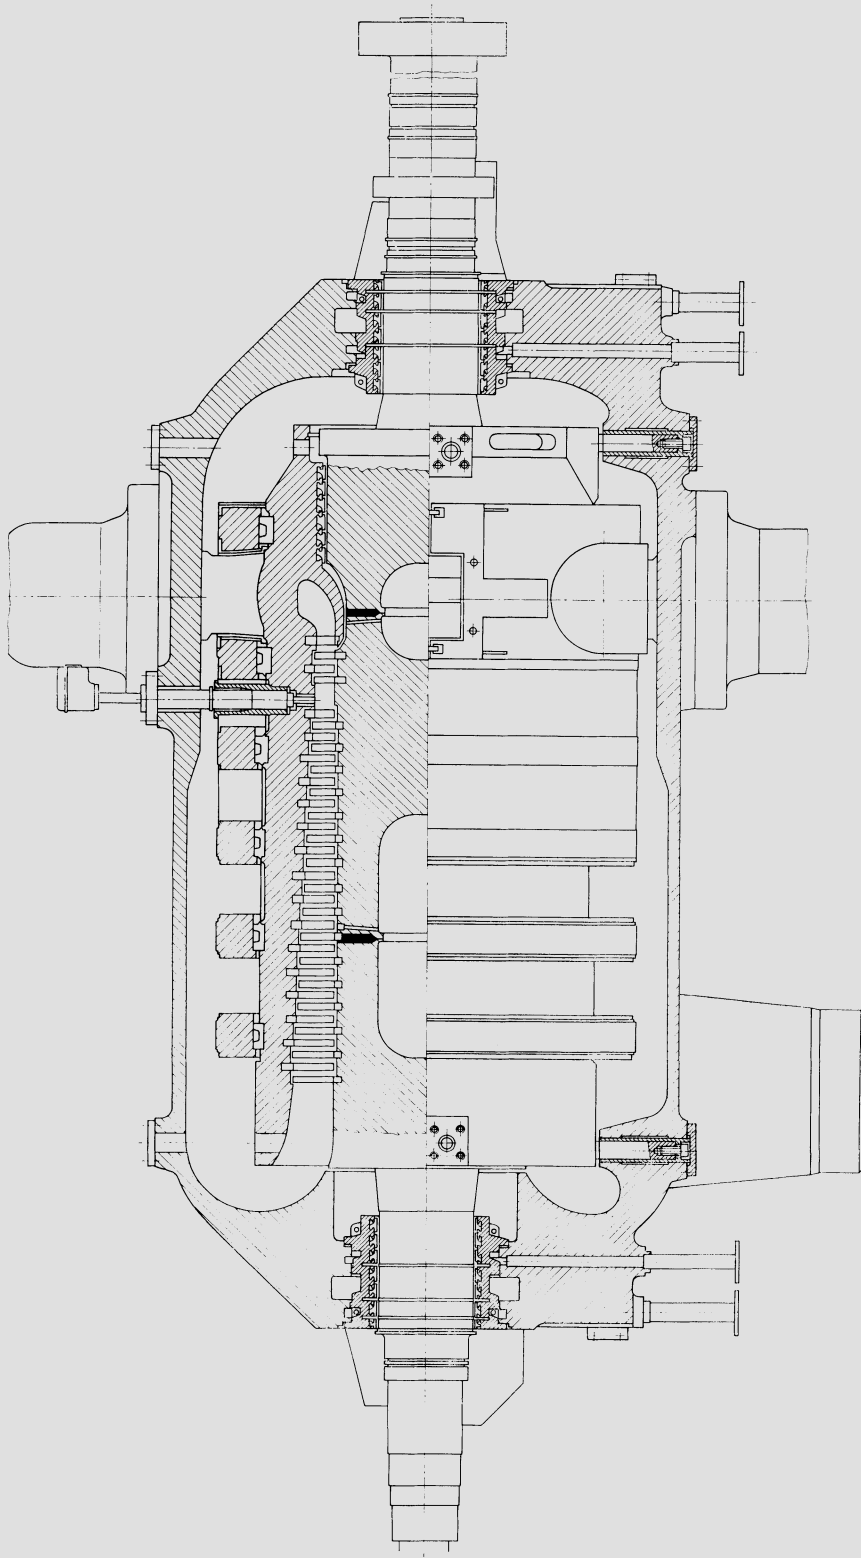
HD-Dampfmaschine von BBC. Geschweißter Trommelrotor. Zweiteiliger flanschloser Leitschaufelträger durch Schrumpfringe zusammengehalten, wärmedämmende Zwischenringe zwischen Leitschaufelträger und Schrumpfringen
